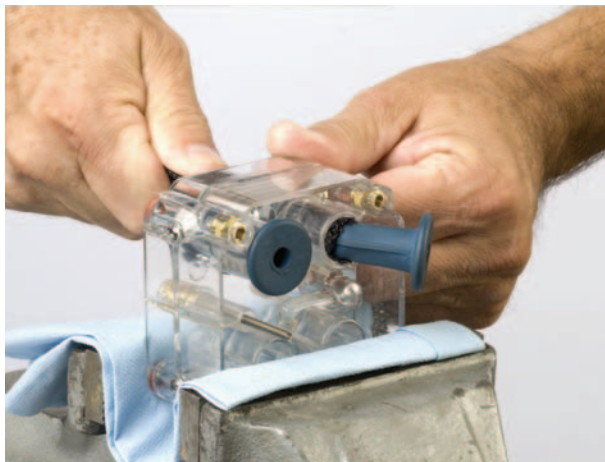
Pinch valve inbrengen in inbrenggereedschap
